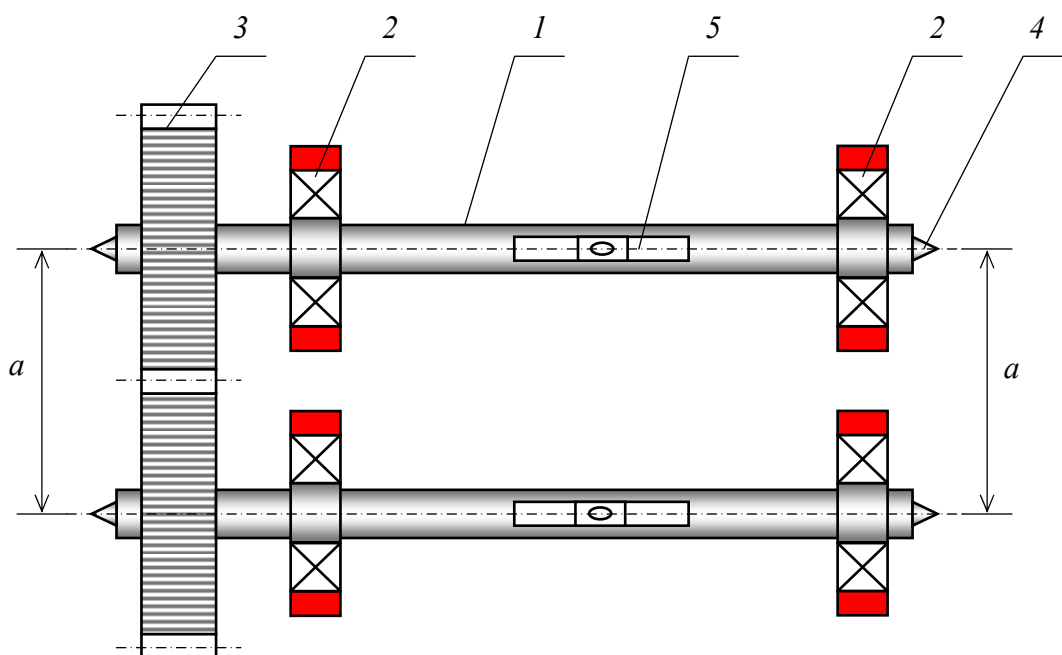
Схема стэнда для выверкн и регулнрования валов и зубчатых передач: 1 – вал; 2 – подшипник качения; 3 – зубчатое колесо; 4 – ввертыш; 5 – уровень
